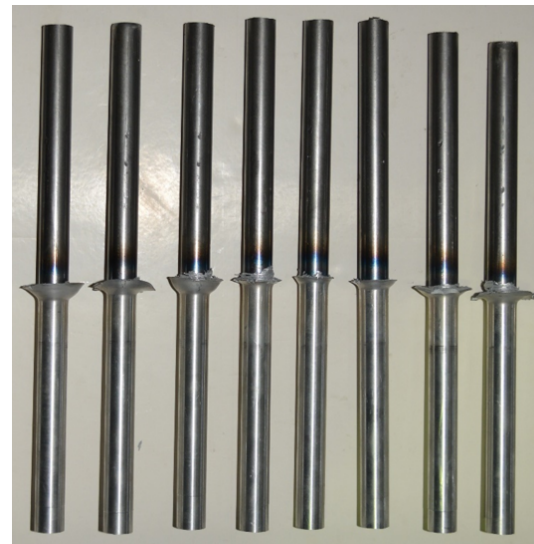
Probetas soldadas, donde se puede observar distintas configuraciones del flash sobre el eje de aluminio
